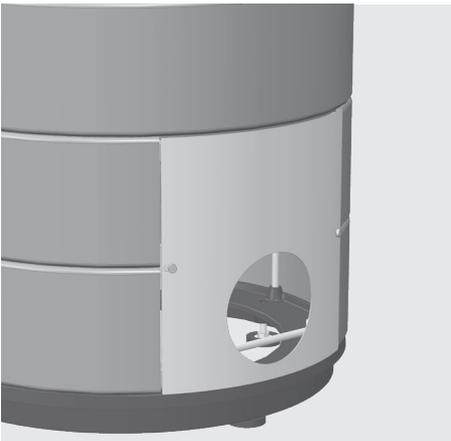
Plaque d'inspection sur la face arrière de l'appareil avec découpe pour le conduit
